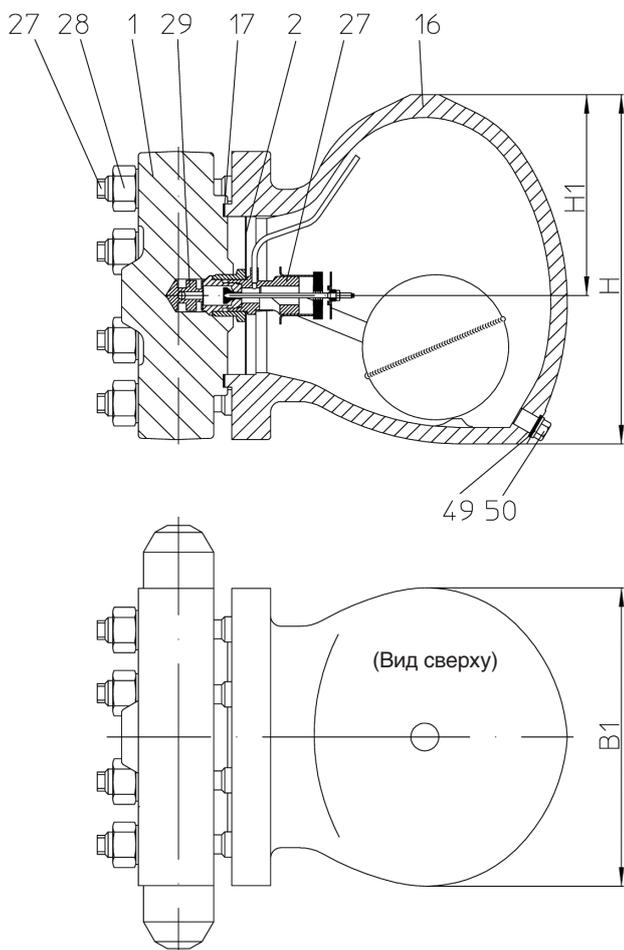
сварка встык – горизонтальная установка
